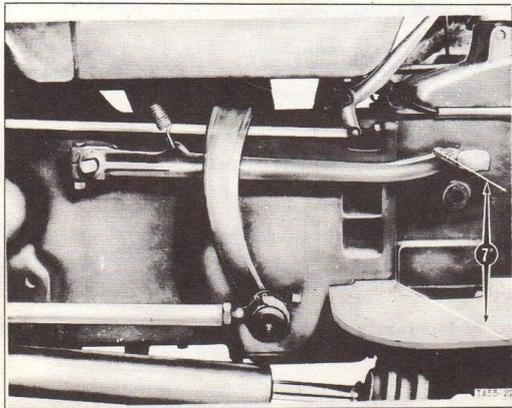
Réglage de la hauteur de la pédale (7") : Distance entre pédale et plancher 177,8 mm
